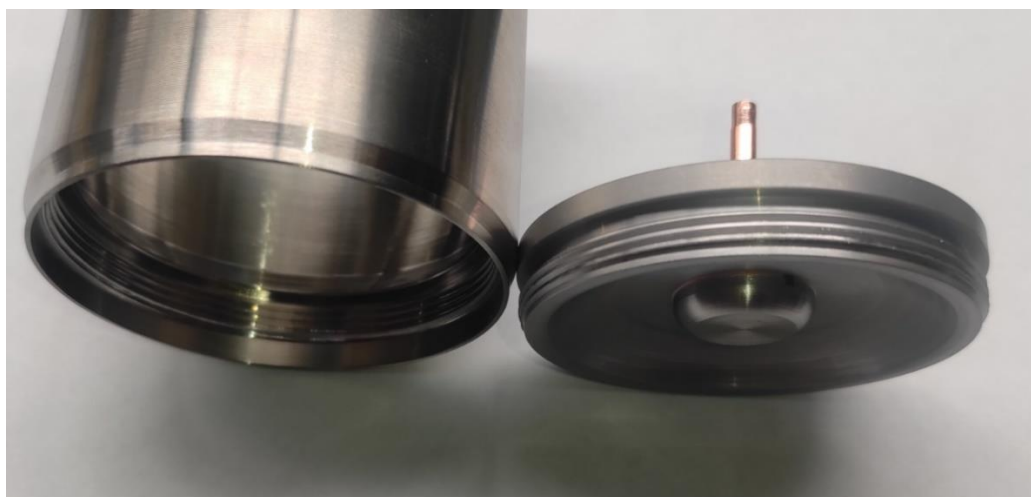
Резьбовое соединение анодной ножки (крышки) с корпусом
